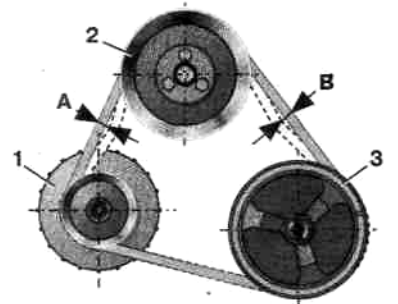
Схема проверки натяжения ремня привода насоса
